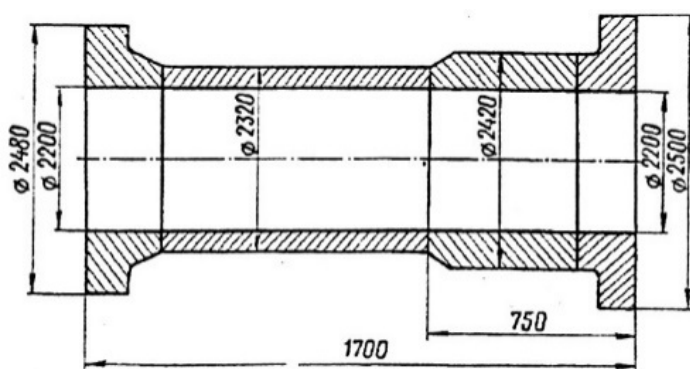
Ескіз корпусу компресора газової турбіни
